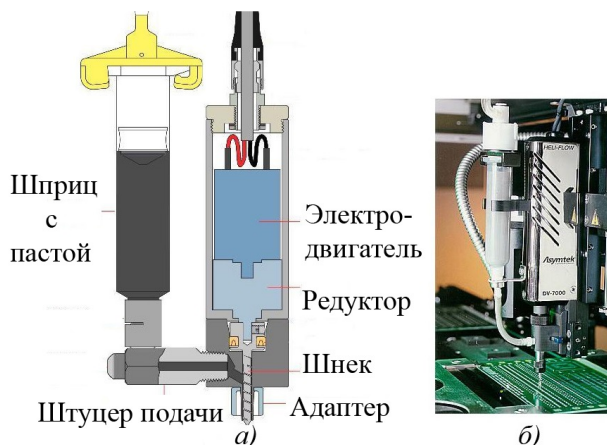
Автоматический дозатор: а – конструкция; б – внешний вид
